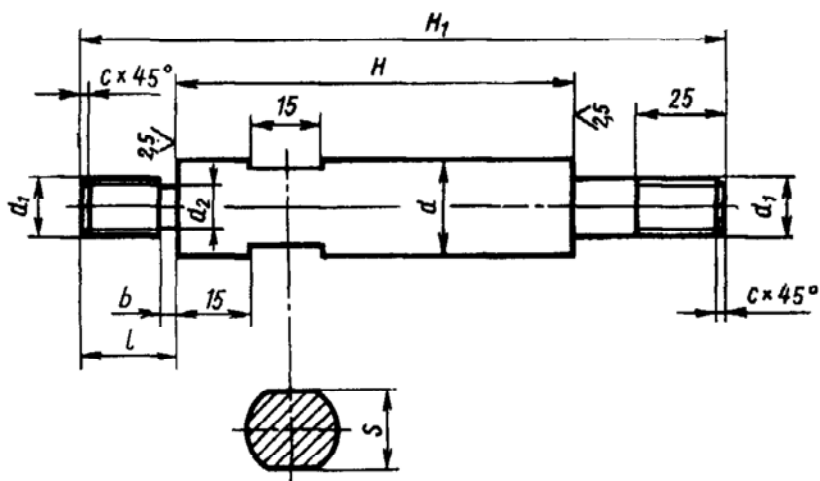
Конструкция стоек пневматического приспособления удаления стержней
